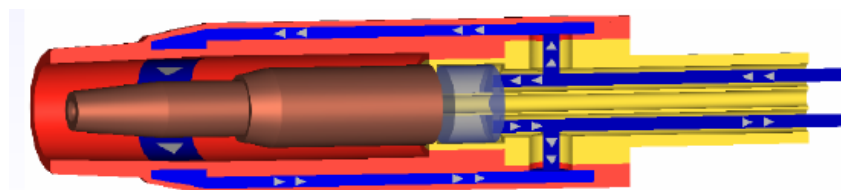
Sistema de refrigeración por agua para antorcha de soldadura.
